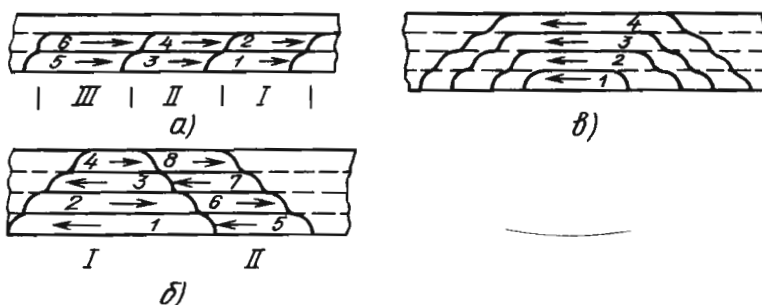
Способы заполнения разделки при сварке толстолистовой стали:
